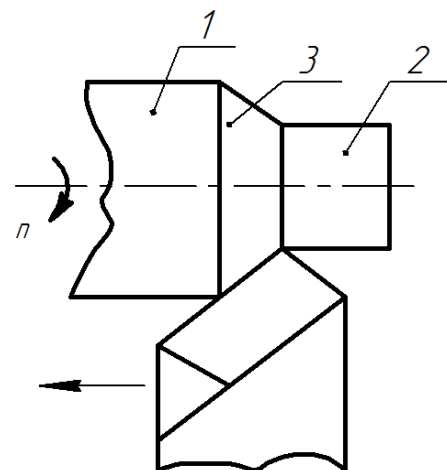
Поверхні на заготовці, яка обробляється точінням
